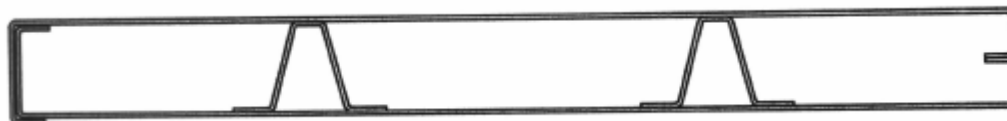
Conjunto painel fechado com dois reforços trapezoidal.
